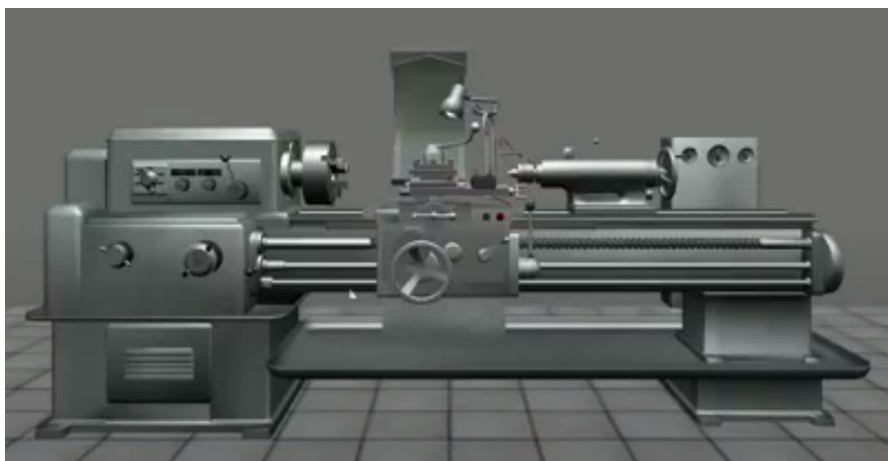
Зовнішній вигляд лабораторного стенда на базі токарного верстата 1К62
